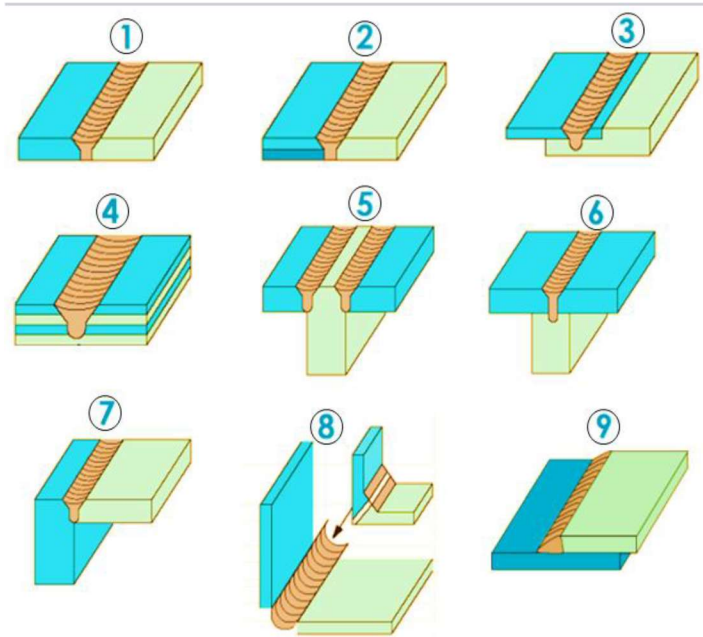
Configurations des joints pour le soudage par friction [7].
